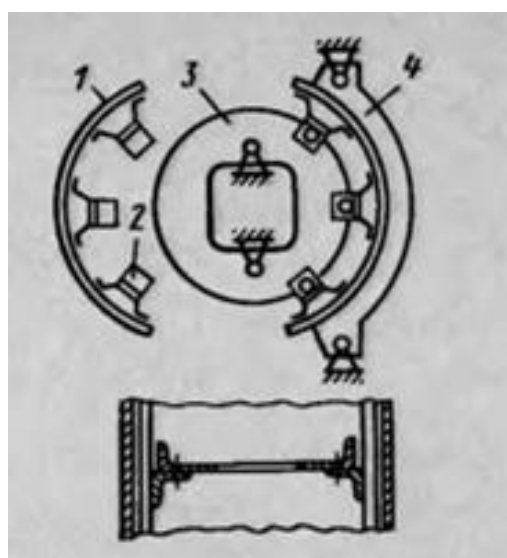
Схема сборки по базе «внешняя поверхность обшивки»:
